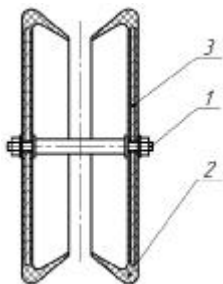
Конструкція вдосконаленого конусного котка: 1 – вісь; 2 – гнучкий гумовий обід; 3 – металевий диск.
